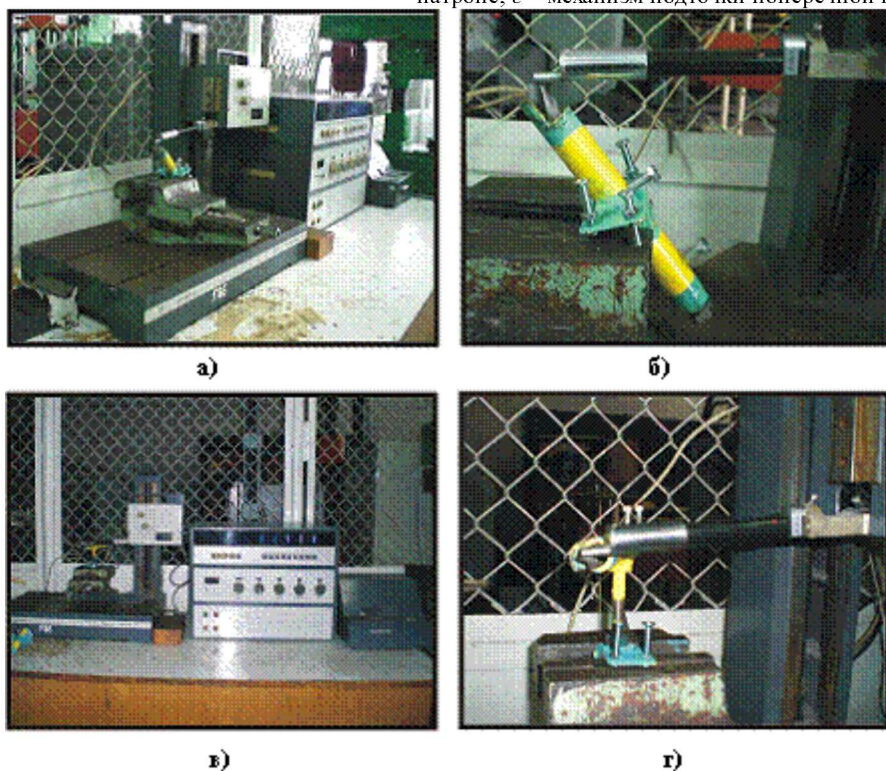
Общий вид профилографа-профилометра и приспособлений для замеров параметров шероховатости на различных поверхностях сверла:
